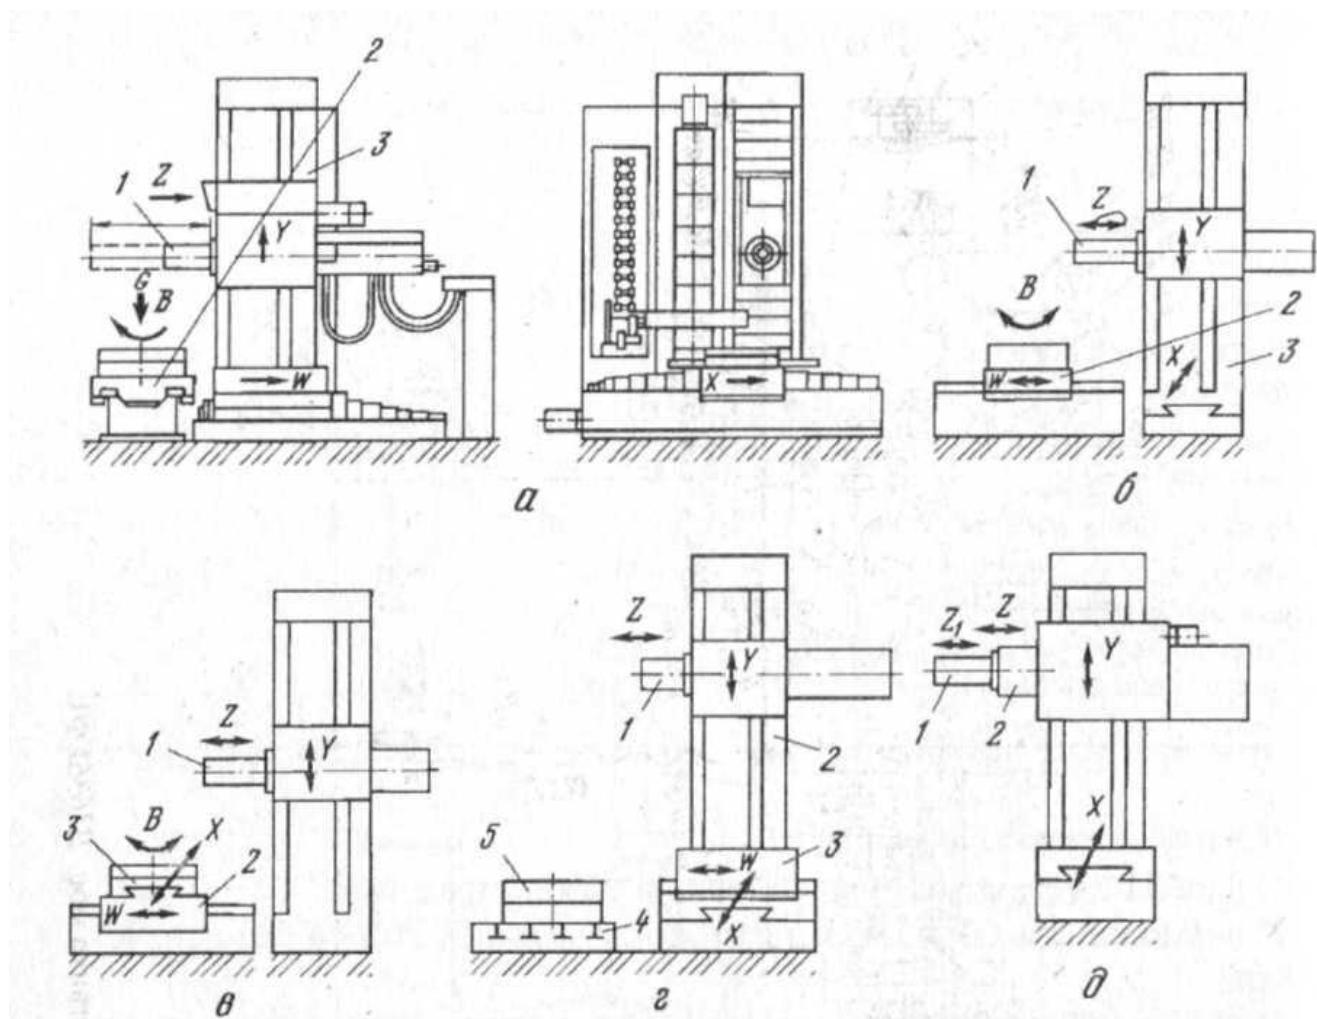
Компоновка горизонтально-расточных станков.
